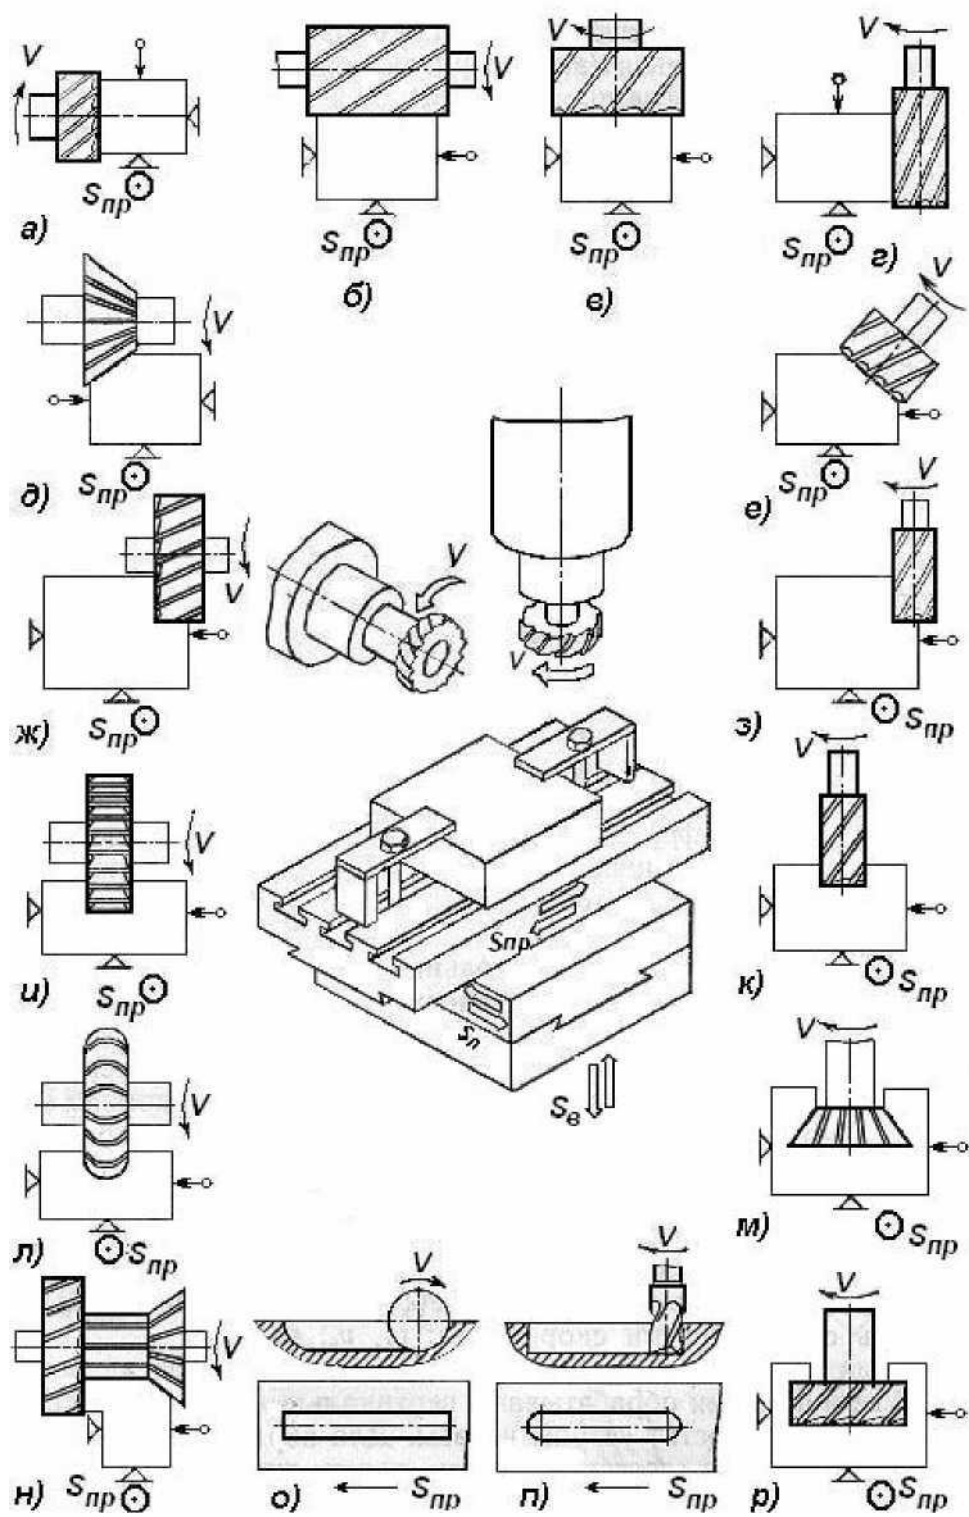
Типы фрез и схемы обработки поверхностей на фрезерных станках: а, в, е - торцевые; б - цилиндрическая; г, з, к - концевые; д - угловая; ж - дисковая; двухсторонняя; и - дисковая трехсторонняя; л - фасонная; м - «ласточкин хвост»; н - набор фрез; о - прорезная; отрезная; п - шпоночная; р - Т-образная
